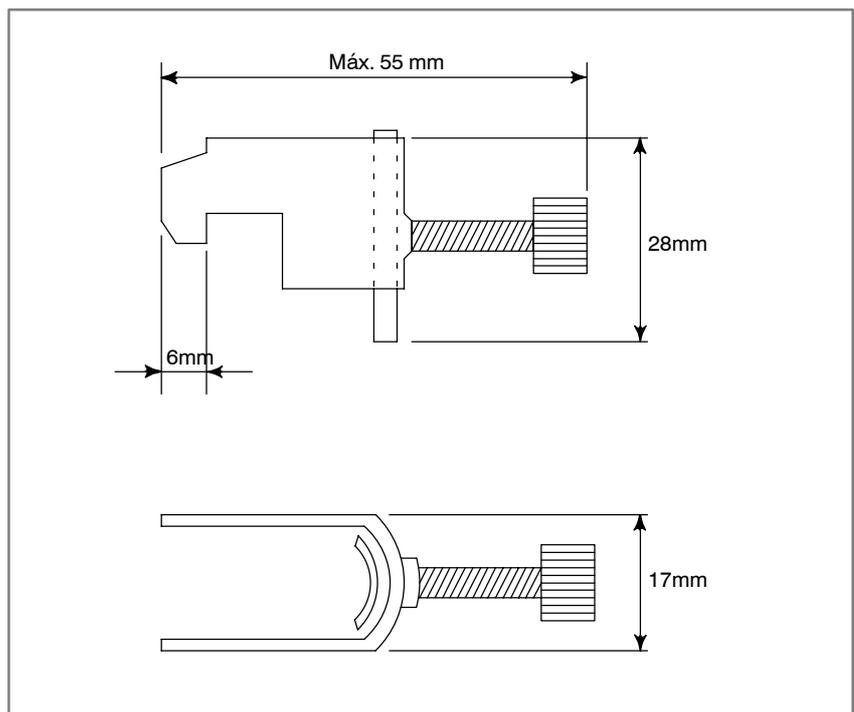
(e) Planos externos de las monturas metálicas para la abrazadera.
